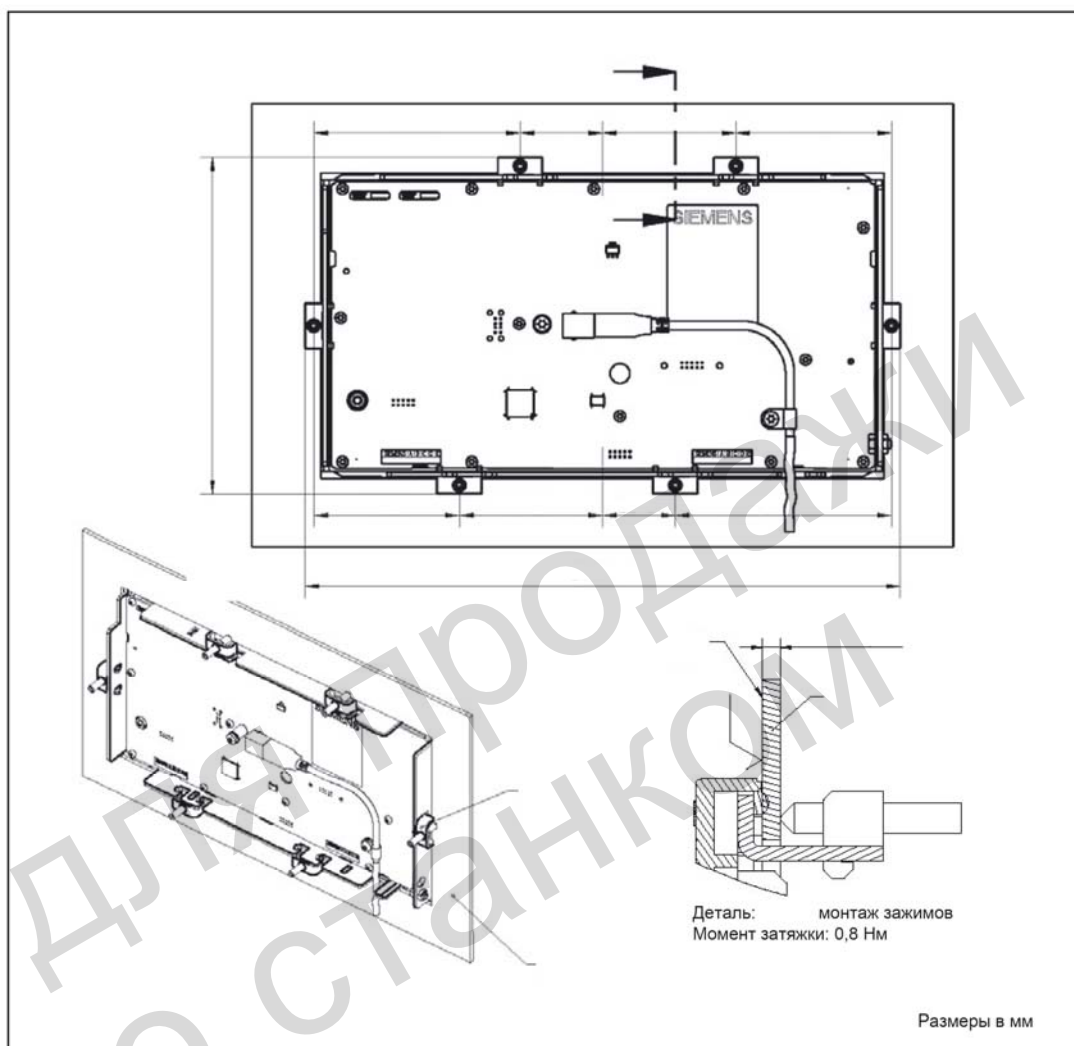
Габаритный чертеж для монтажа полной клавиатуры ЧПУ KB 310C
